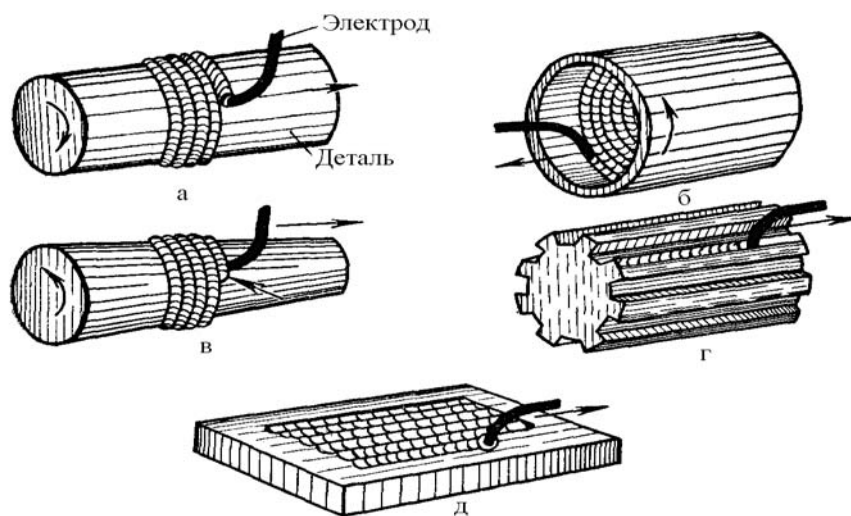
Типы деталей, восстановленных вибродуговой наплавкой [4]:
